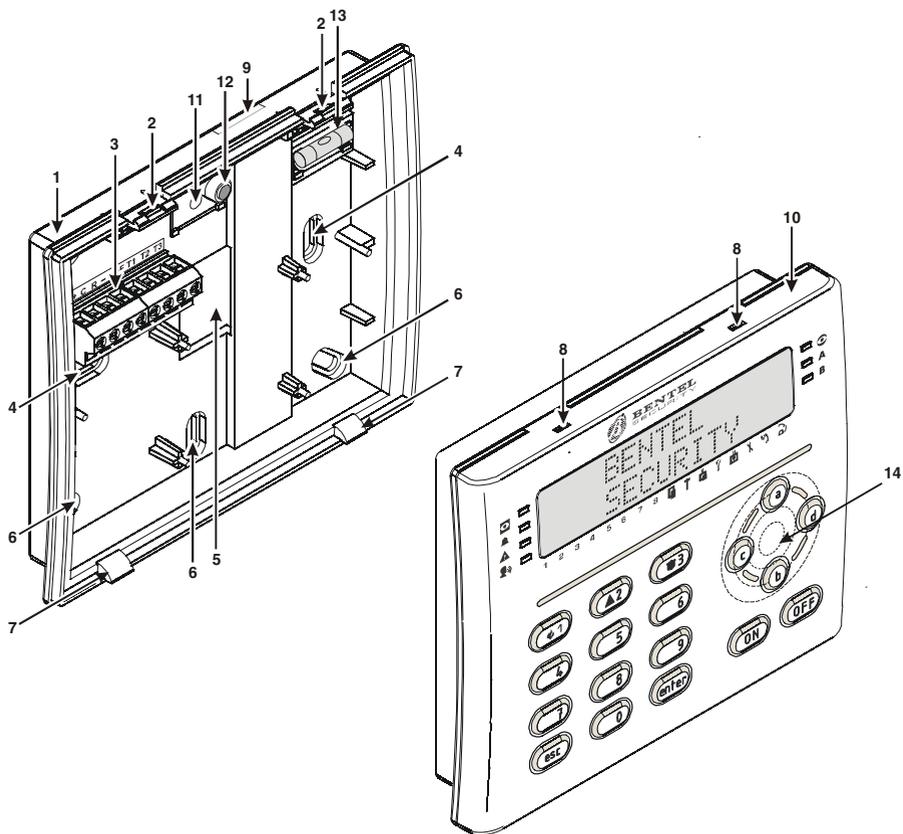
Parti della tastiera - Keypad Parts - Partes del teclado - Composants de clavier
